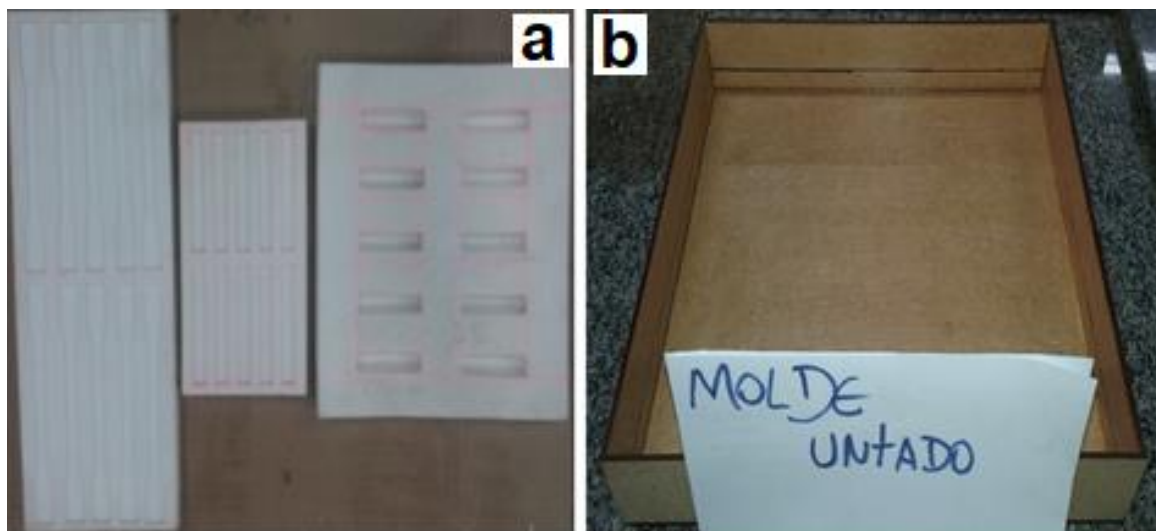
Molde de silicone (a) molde em madeira MDF (b)
